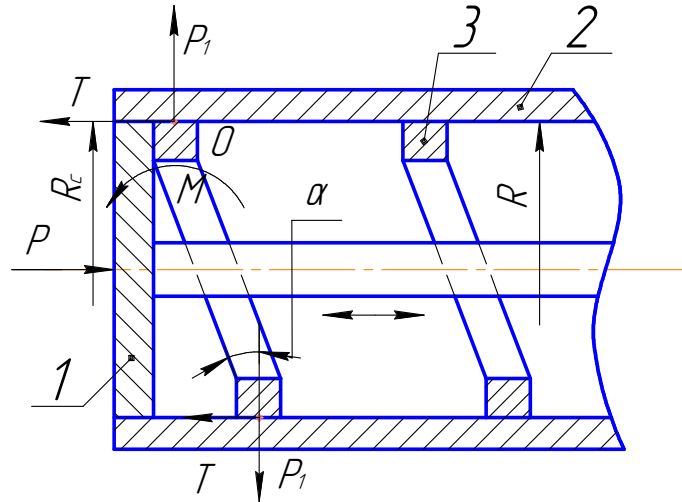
Розрахункова схема дії сил затиску циліндричної заготовки гвинтовим елементом:
